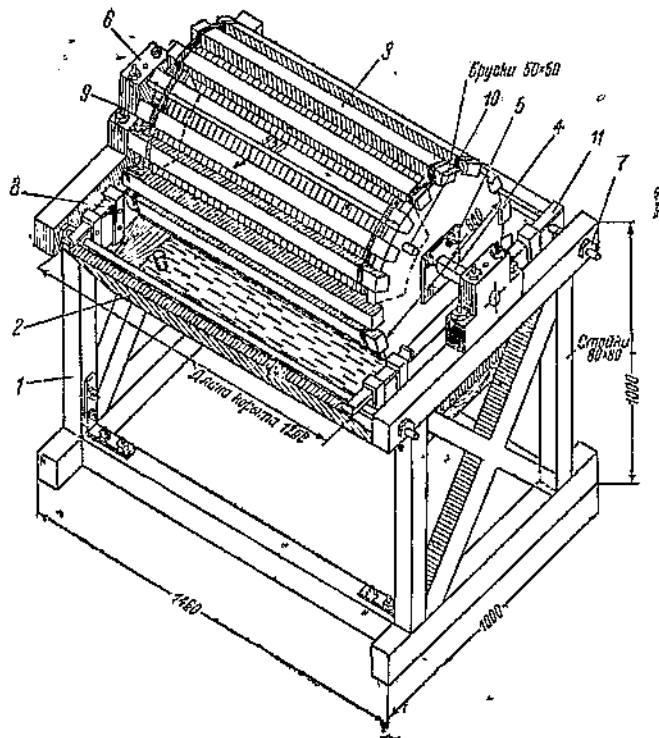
Барабанная мойка: 1—стапина; 2—корыто; 3—барабан; 4—ось барабана; 5—накладки барабана; 6—подшипники; 7—болты для корыта; 8—запор для корыта; 9—съемная часть барабана; 10—штыри для закрепления съемной части барабана; 11—петли корыта
